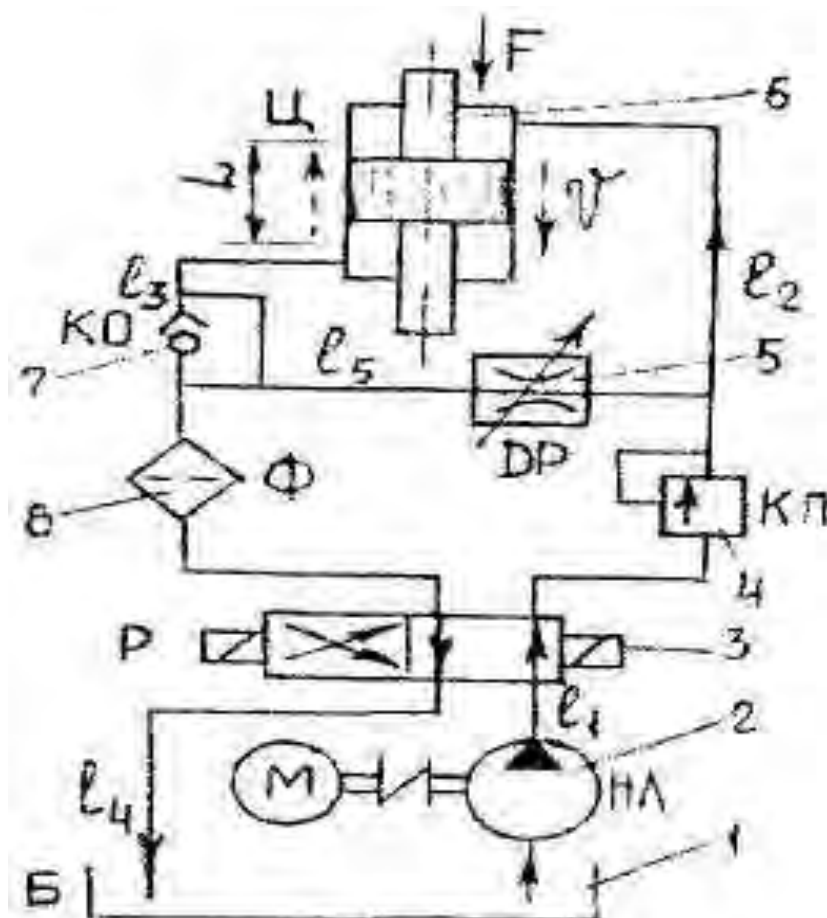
Схема перемещения бабки плоскошлифовального станка модели 3Б722
